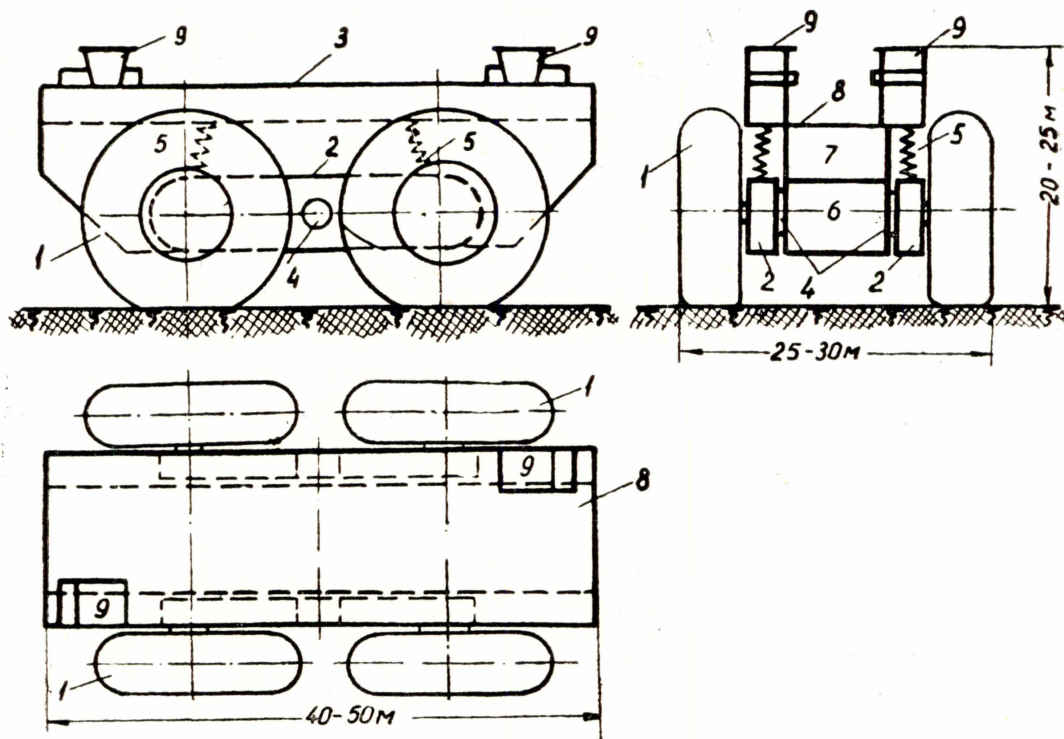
Схема большеколесного вездехода с колесами диаметром 15—20 м. 1 — колеса; 2 — балки-балансиры; 3 — платформа; 4 — оси; 5 — амортизаторы; 6, 7, 8 — нижний, средний и верхний ярусы платформы; 9 — кабины управления.
